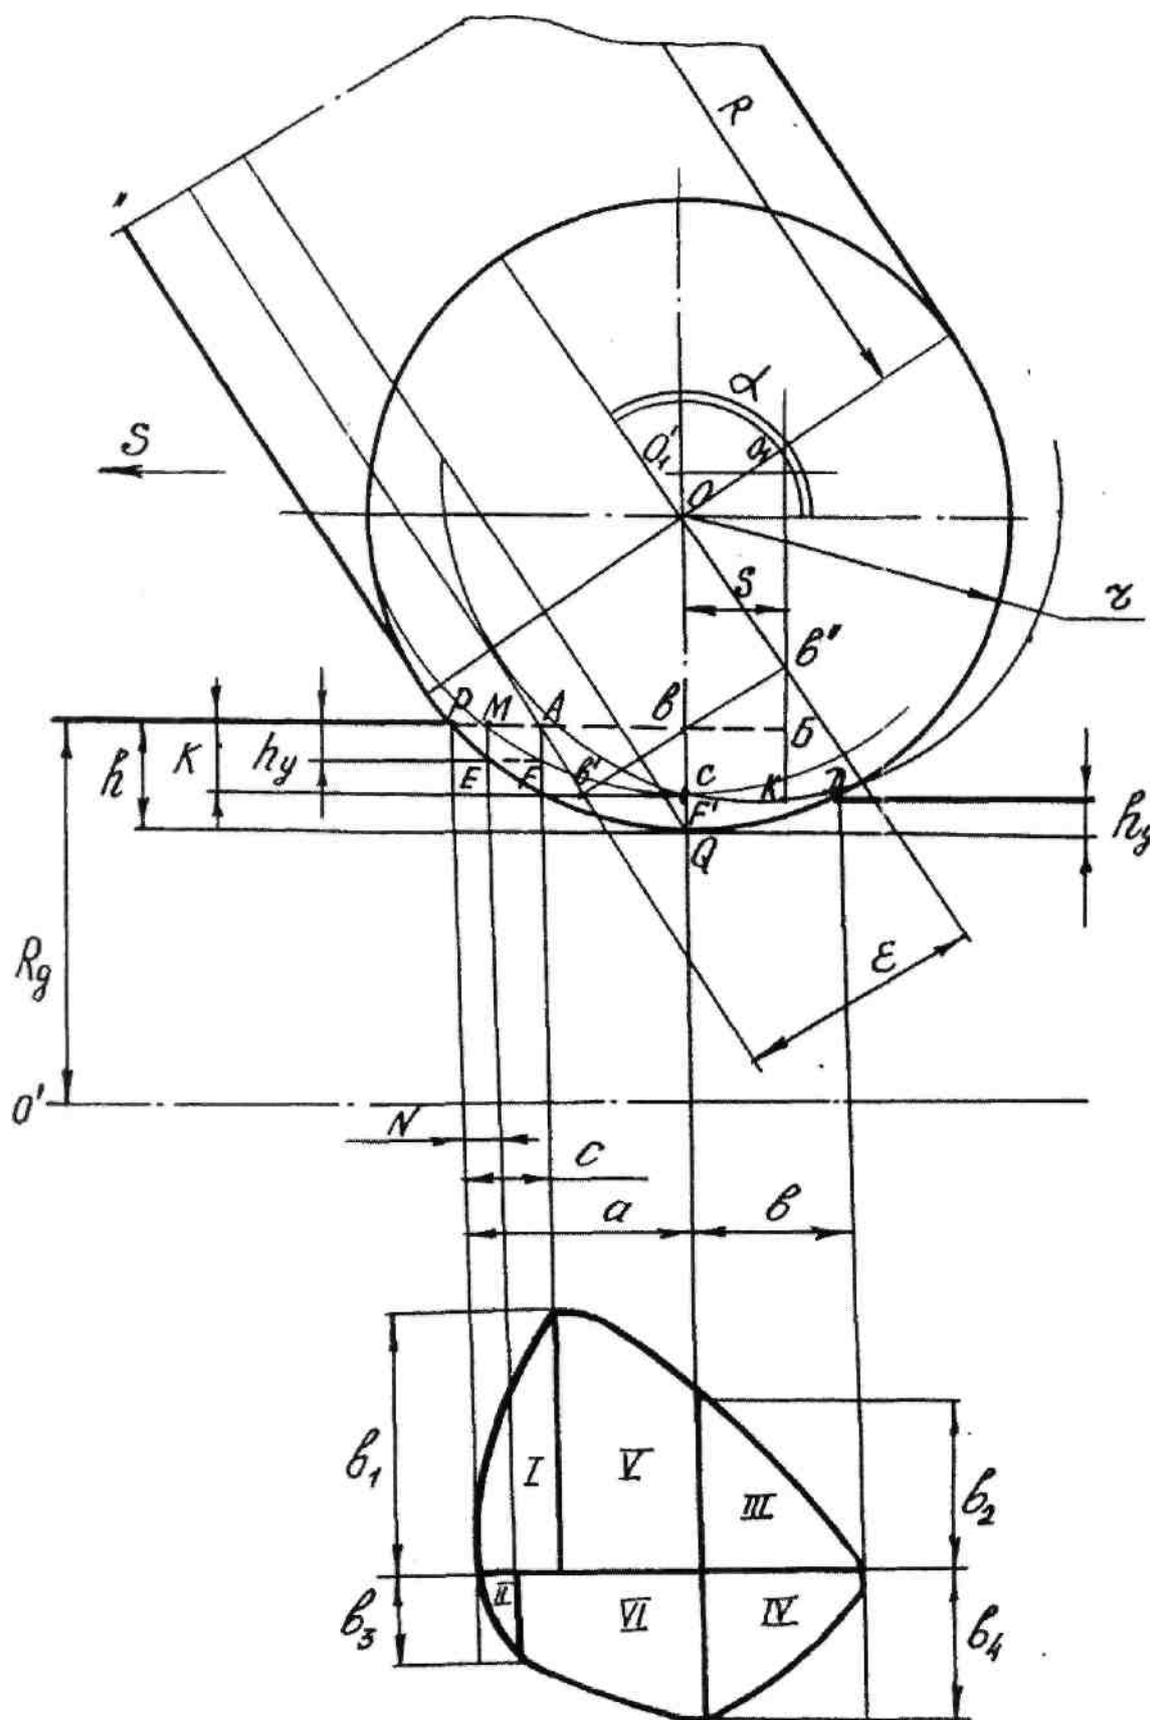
Схема для расчета пятна контакта деформирующего ролика с цилиндрической поверхностью
